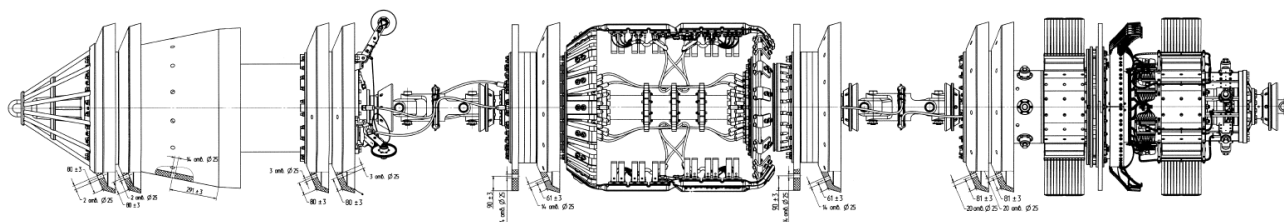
Чертеж общего вида дефектоскопа внутритрубного комбинированного магнитно-ультразвукового 40-ДМУ.01-00.000 в типоразмере 1067 мм (42")
